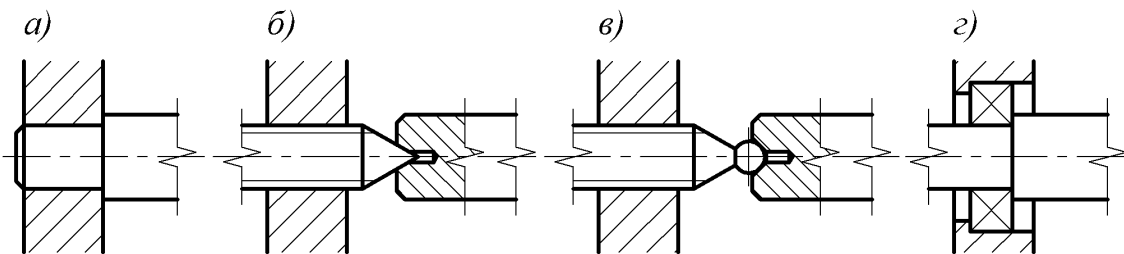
Подвижные соединения для вращательного движения – опоры:
